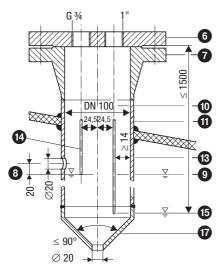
Tubo di calma di protezione (da prevedere sul posto) per installazione all'interno della caldaia previsto per montaggio di un secondo apparecchio GESTRA
